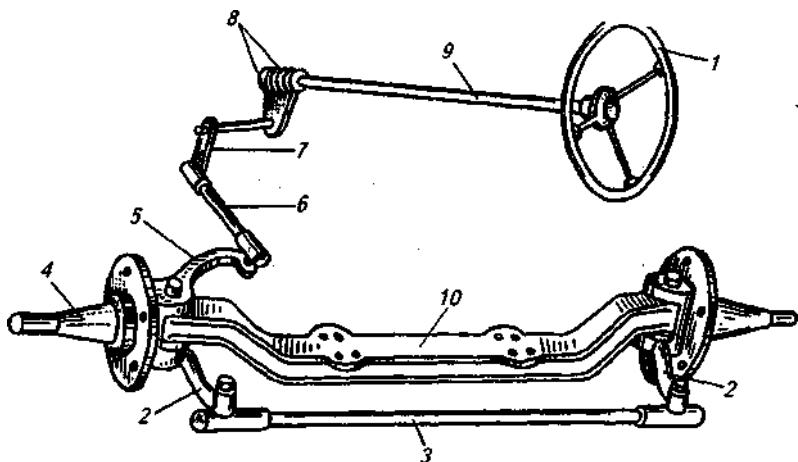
Схема рулевого управления при зависимой подвеске: 1 —рулевое колесо; 2—поворотные рычаги; 3 — поперечная тяга; 4—поворотная цапфа; 5—рычаг; 6—продольная тяга; 7—сошка; 8—редуктор рулевого механизма; 9—рулевой вал; 10—балка моста
